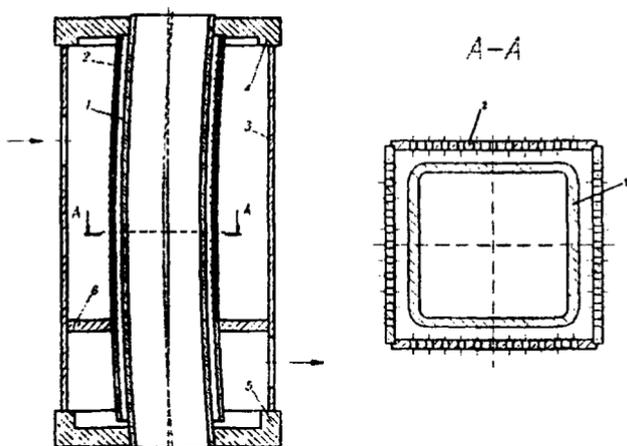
Схема струйного охлаждения кристаллизатора МНЛЗ: 1 – кристаллизатор; 2 – экран; 3 – цилиндр; 4 – верхний фланец; 5 – нижний фланец; 6 – перегородка
